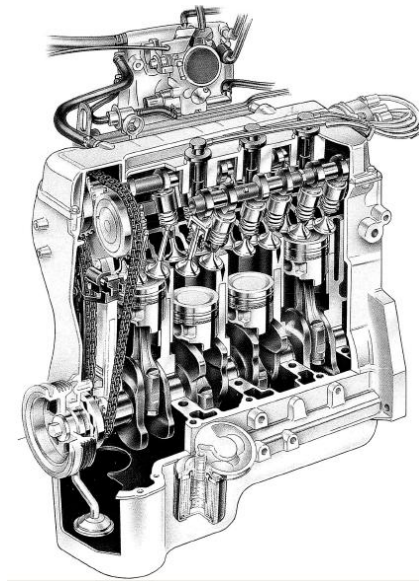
(Esquema en corte del motor K10A DOHC del Chevrolet Alto)
